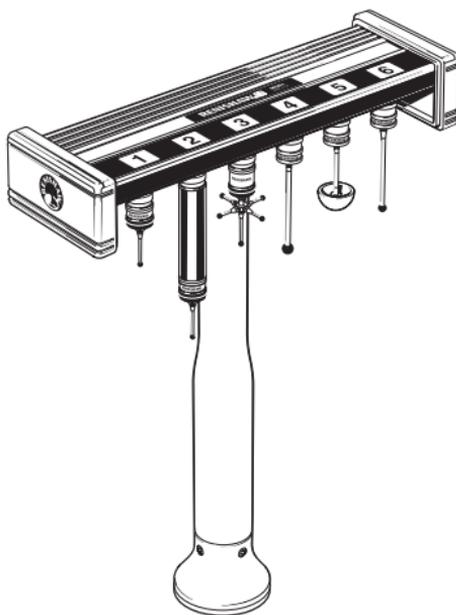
El kit de almacenamiento MSR1 - Montaje en mesa de CMM (módulos y palpadores no incluidos)
